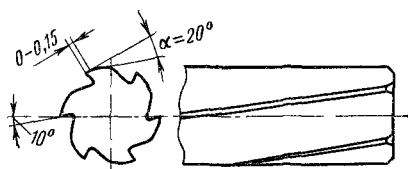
Развертка для развертывания отверстий в магниевых сплавах
